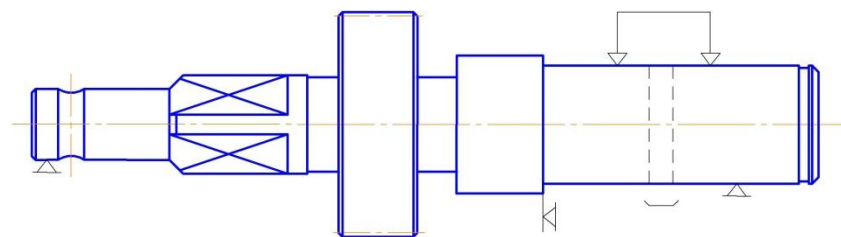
Ескіз обробки деталі на 055 операції.
